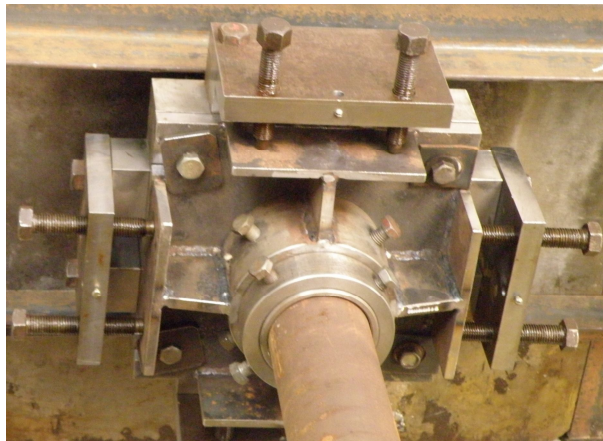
Общий вид опорного приспособления (верхняя опора)
